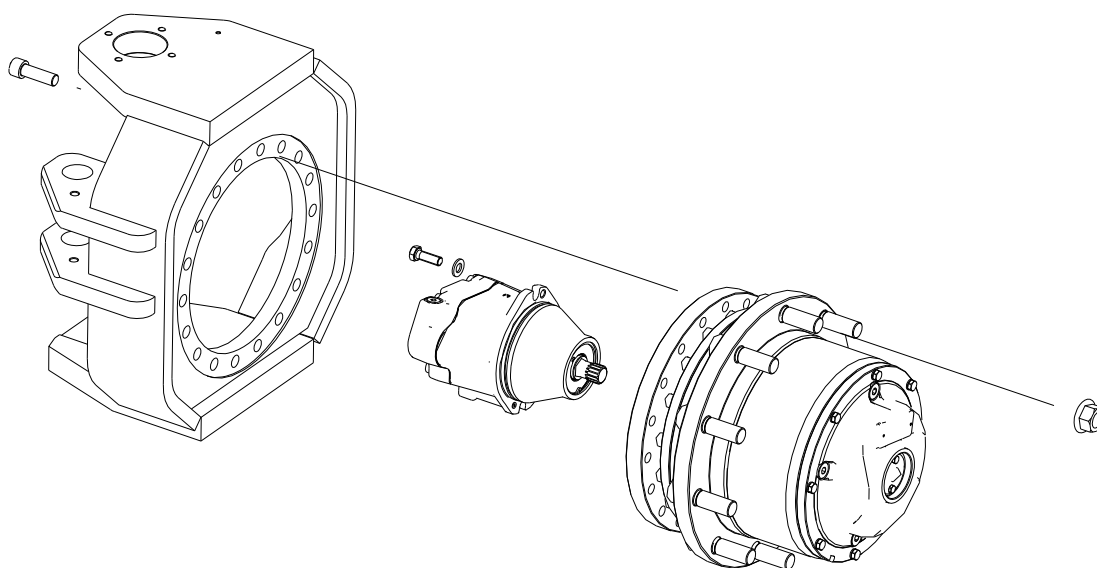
Diagrama de desmontagem do motor de deslocamento
